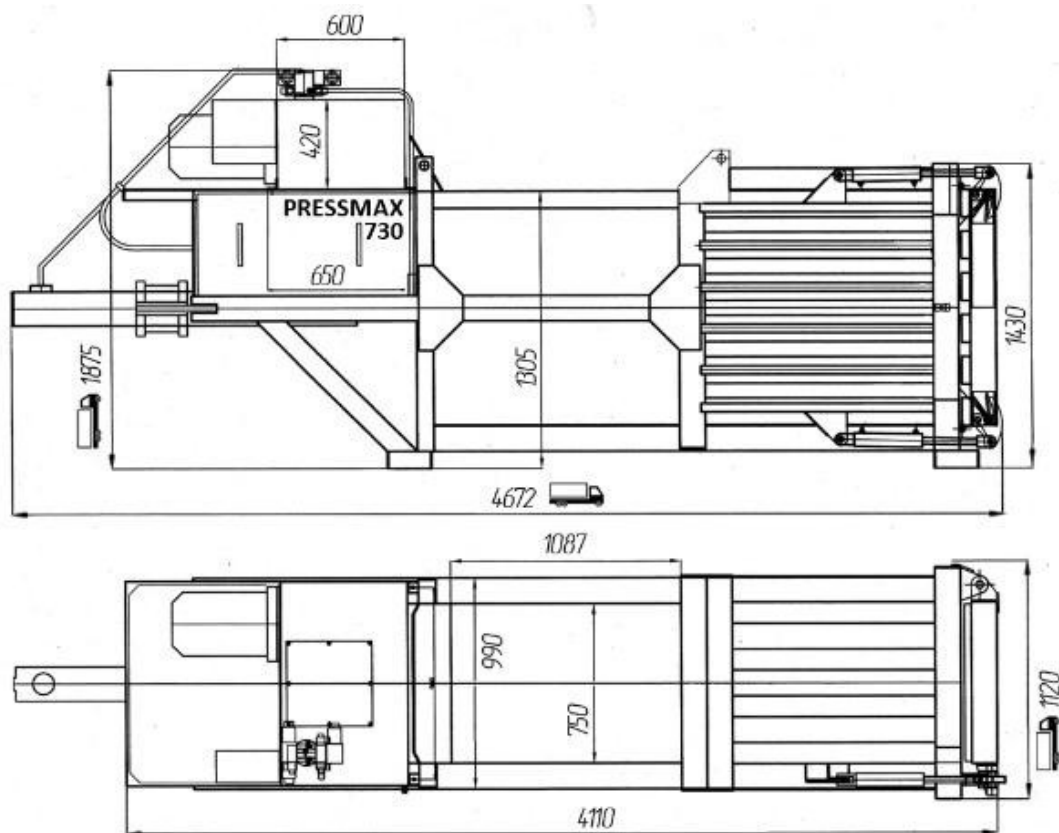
Гидравлический горизонтальный пакетирующий пресс
